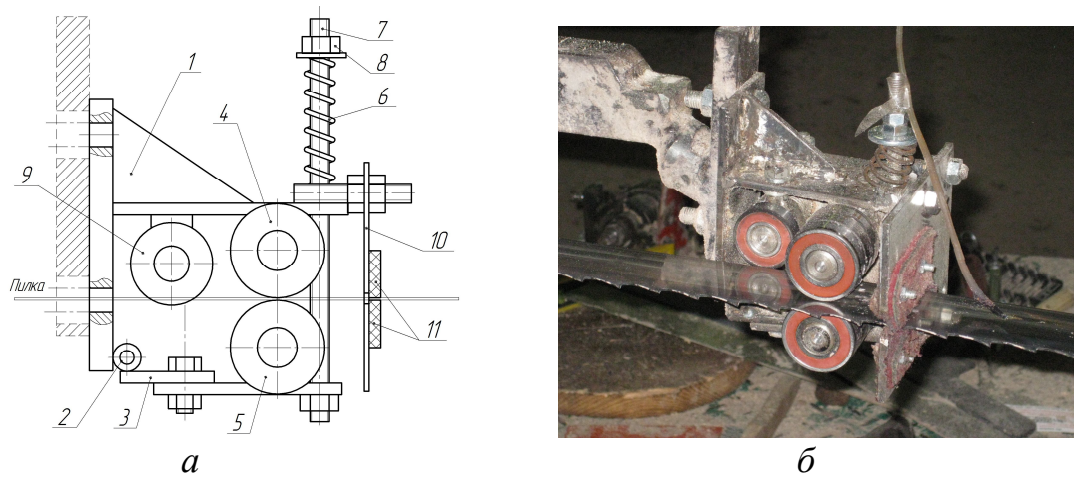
Дослідний взірець двобічних контактних напрямників стрічкової пилки для верстата СКТП 505-2: а – креслення конструкції; б- загальний вигляд (1 – копус; 2 – шарнір; 3 – маятник; 4, 5 – напрямні ролики; 6 – пружина; 7 – шпилька; 8 – гайка; 9 – упорний ролик; 10 – щиток; 11 – ущільнення
